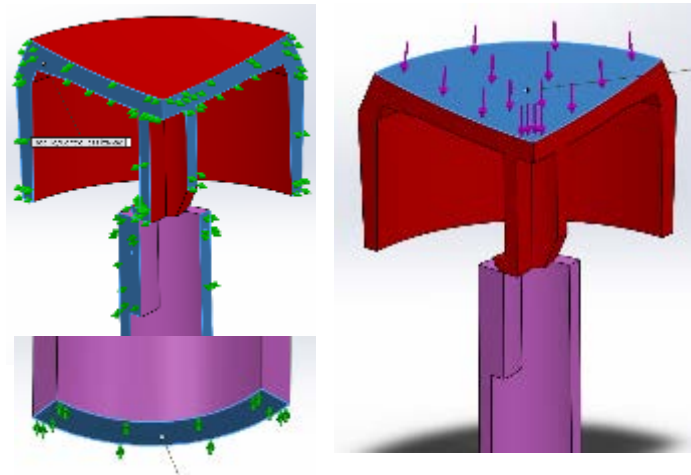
Condiciones de frontera para el ensamble botón/extensión.
